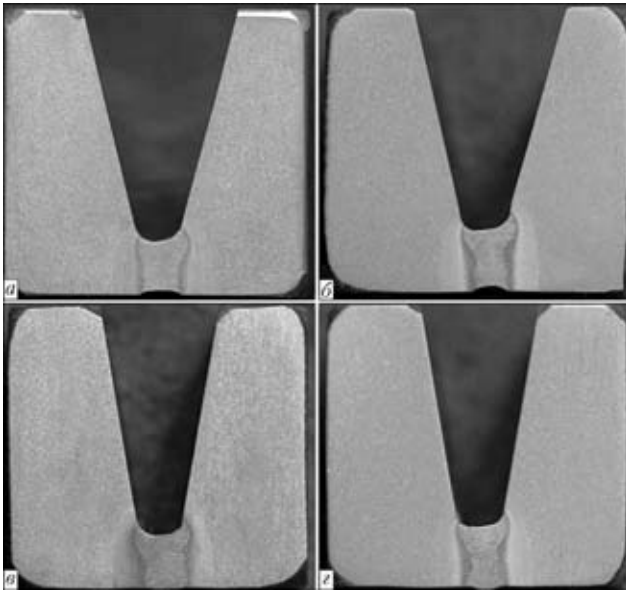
Макрошлифы корневого шва, выполненного лазерной сваркой с V- (а, б) и U-образной (в, з) разделкой и притуплением 5 мм
